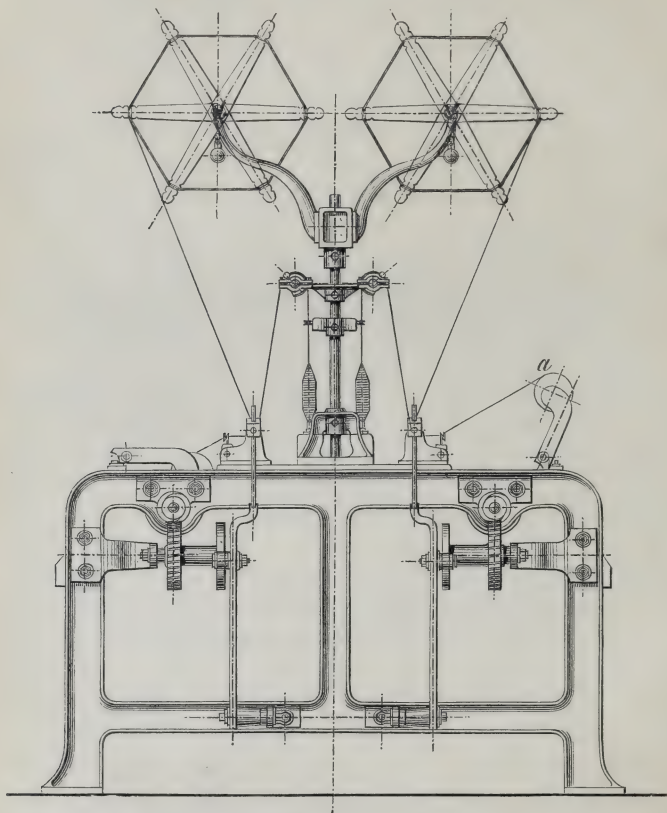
Kettenspulmaschine mit liegenden Spindeln: Seitenansicht.
